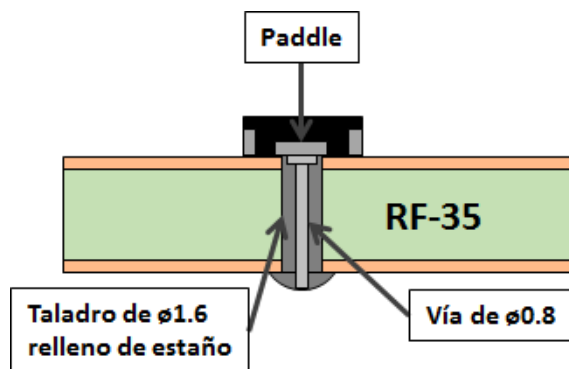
Soldadura del *paddle* de tierra del conmutador
